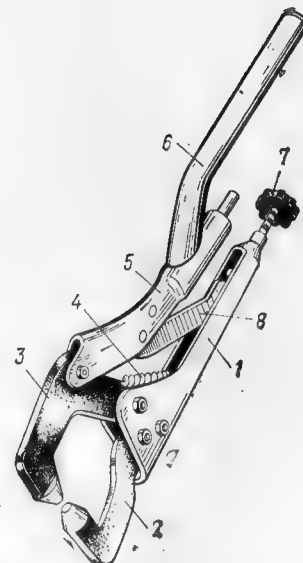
1 — корпус; 2 — губка нижняя; 3 — губка верхняя; 4 — пружина растяжения; 5 — кожух; 6 — ручка; 7 — винт регулировочный; 8 — упор
